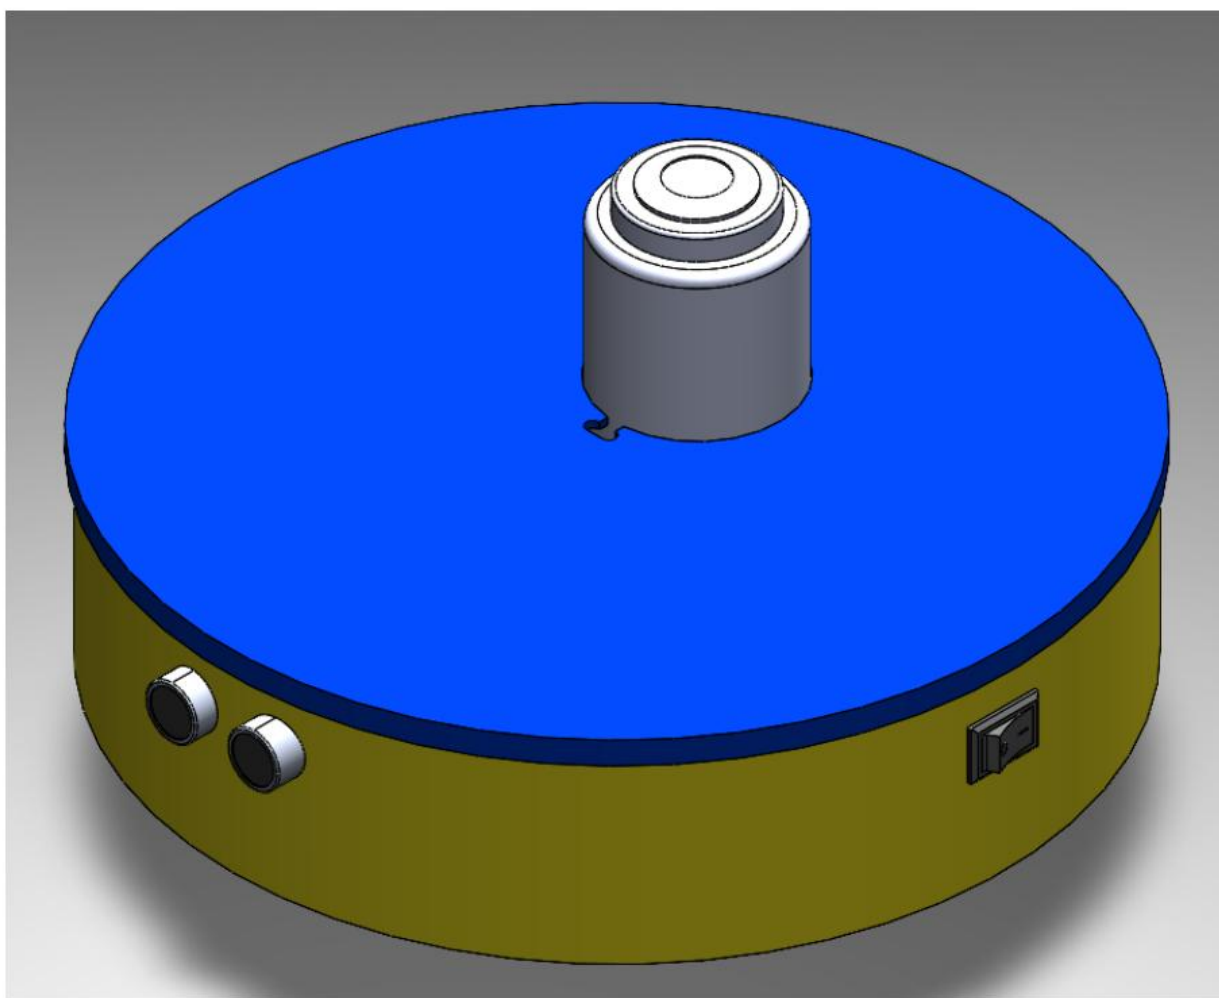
Загальний вигляд 3D-моделі збірки дезінфектора
